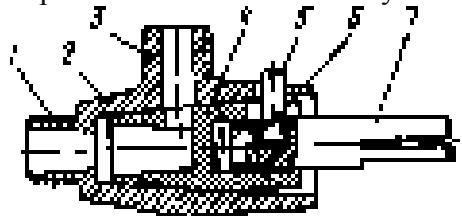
Унифицированный пробковый кран газовой плиты: 1 - штуцер для присоединения к газопроводу; 2 - корпус; 3 - штуцер для присоединения к коллектору; 4 - пробка; 5 - стопорный винт; 6 - пружина; 7 - стержень В последние годы производятся 4-конфорочные газовые плиты повышенной комфортности, оснащенные термоэлектрическим клапаном, терморегулятором и устройством пьезозажигания. По габаритным размерам они отличаются от унифицированных, например, объем духового шкафа для плиты ПГ4-ВК увеличен до 70 дм³.
